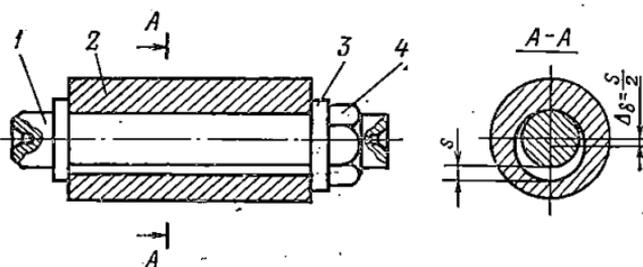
Схема образования погрешности базирования при установке заготовки на цилиндрической оправке с зазором:
